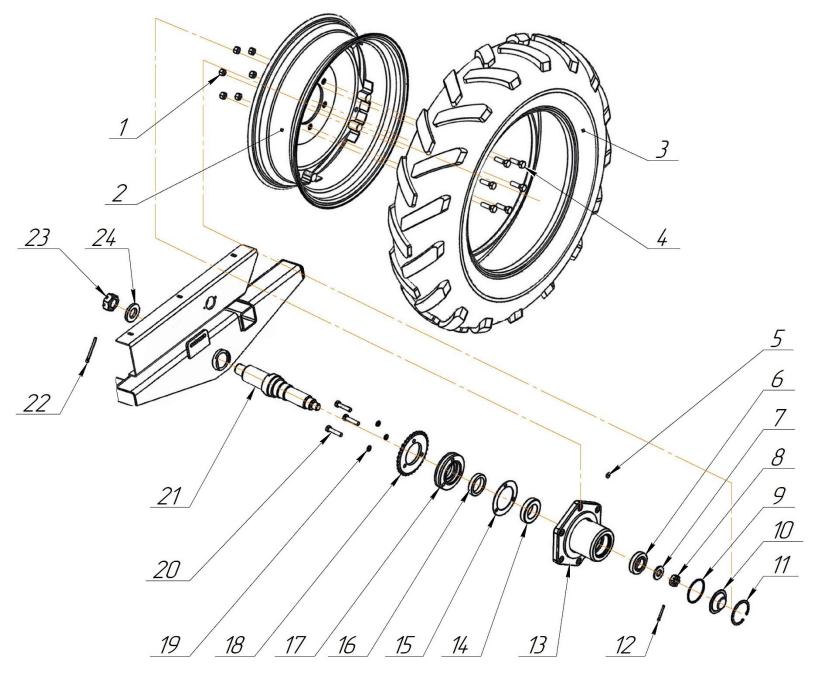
Колесо опорно-приводное и ступица СЗМ 00.2000-01 в сборе
